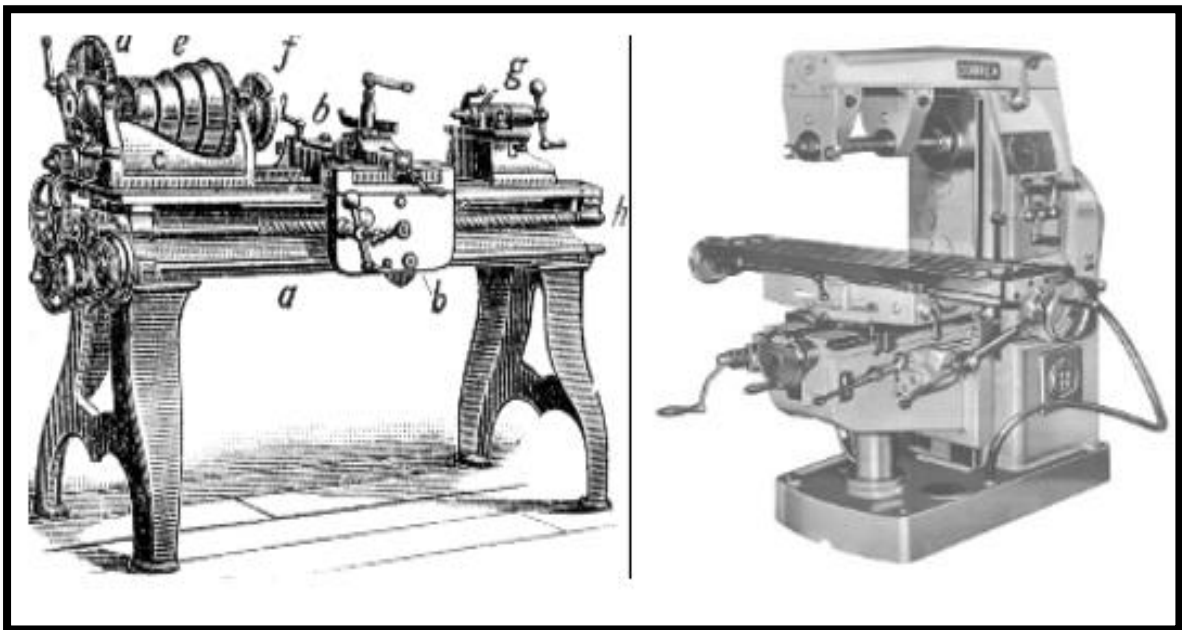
Un tour en 1911, type de machine-outil utilisée pour fabriquer d'autres machines
